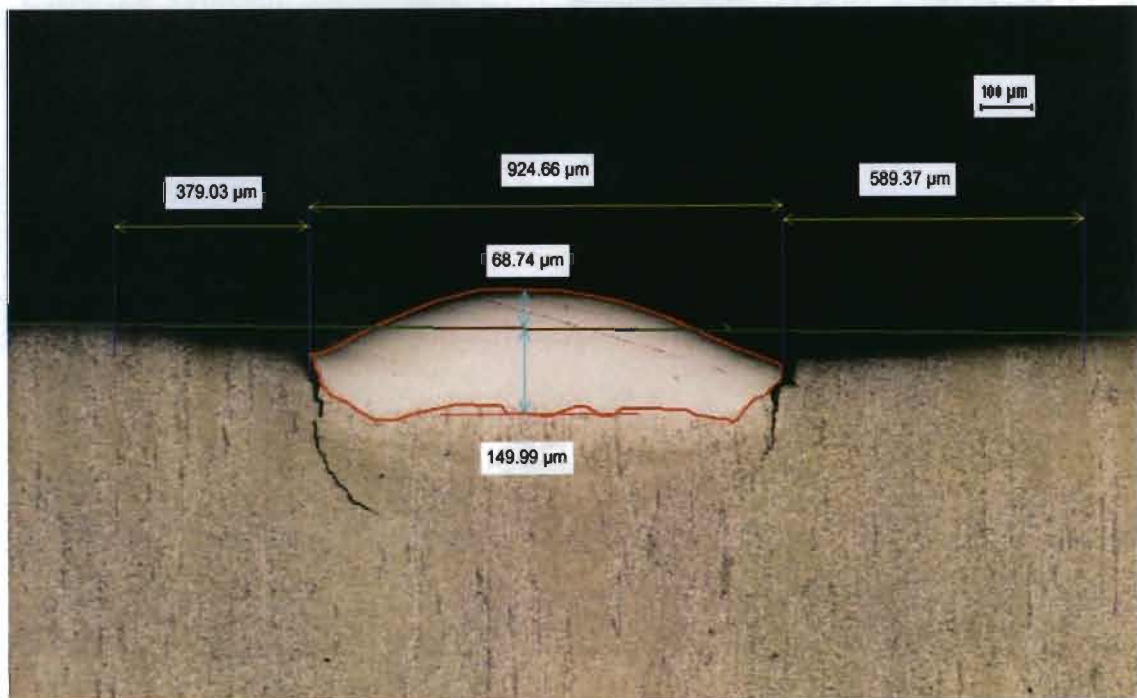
5 Cordón de soldadura 1 visto a 5X
